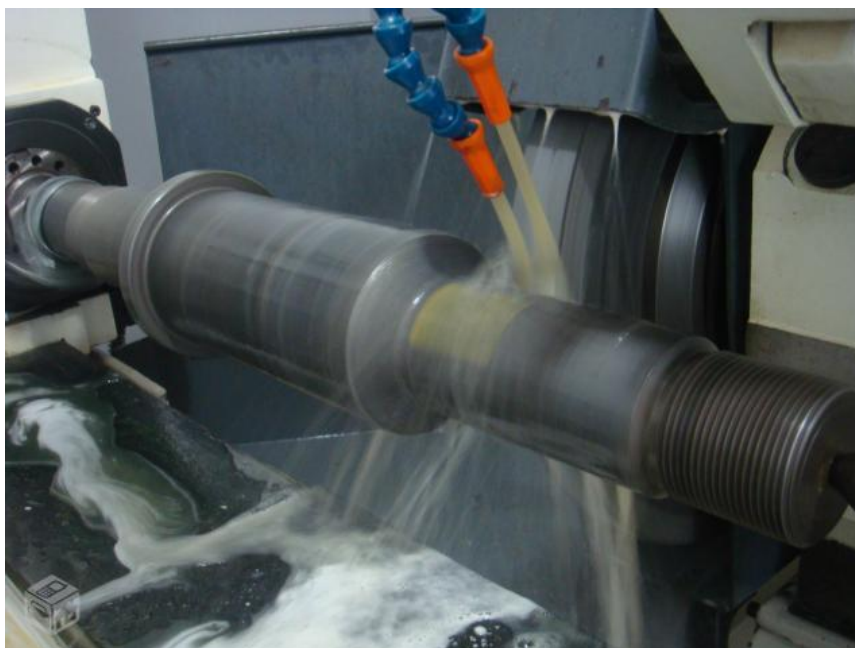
Exemplo de operação numa retificadora cilíndrica universal [57]
